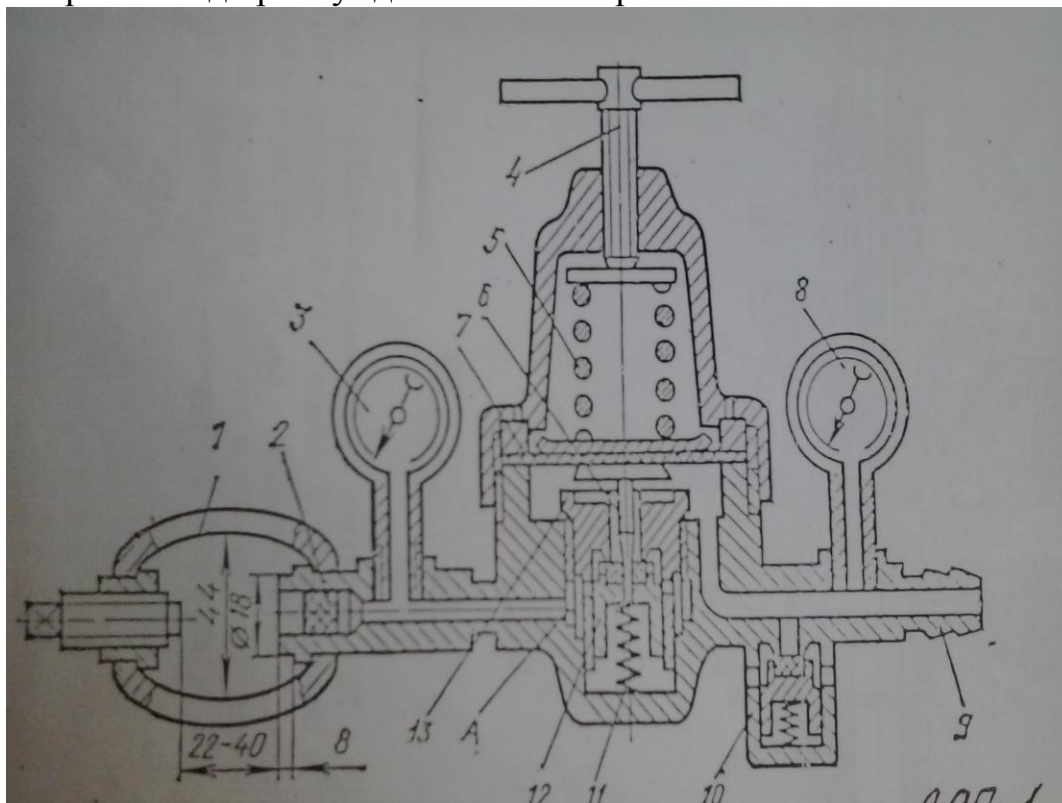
Схема ацетиленового редуктора ДАП – 1
